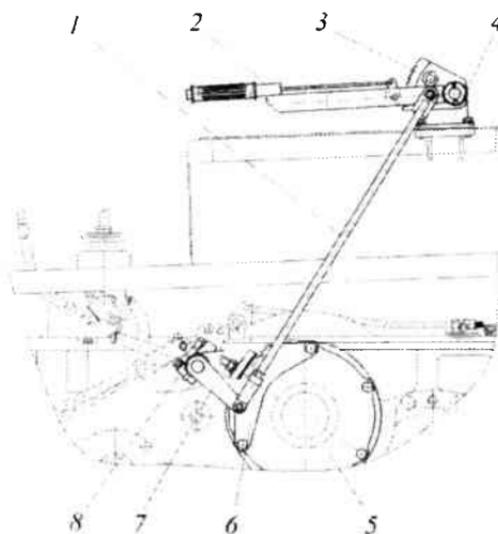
Управление стояночным тормозом: 1 – тяга; 2 – рычаг с рукояткой; 3 – сектор; 4 – кронштейн рычага; 5 – тормоз стояночный; 6 – кронштейн валика; 7 – валик с рычагом; 8 – рычаг тормоза
